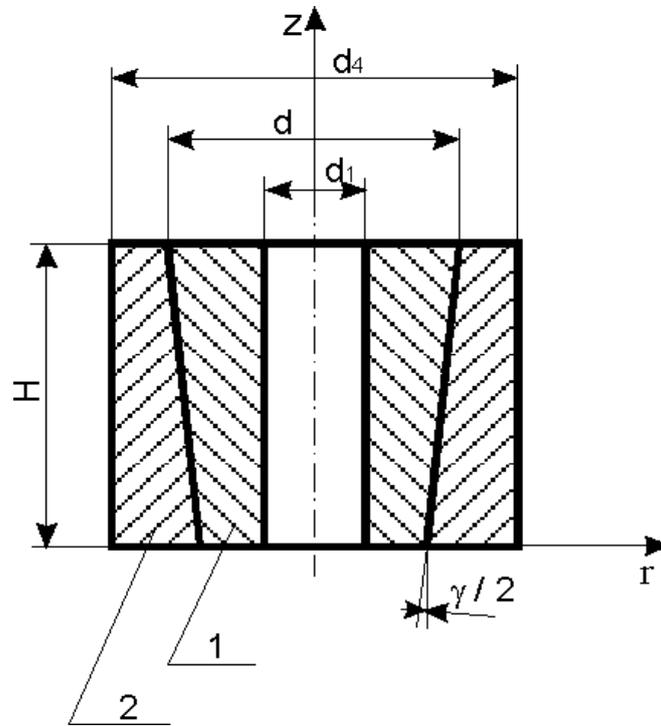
Схема сварного соединения с внешней обоймой
